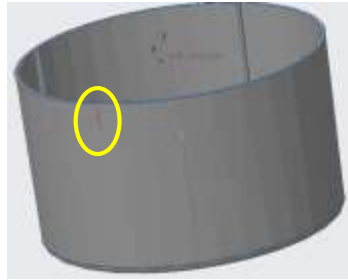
Líneas de soldadura primer análisis
